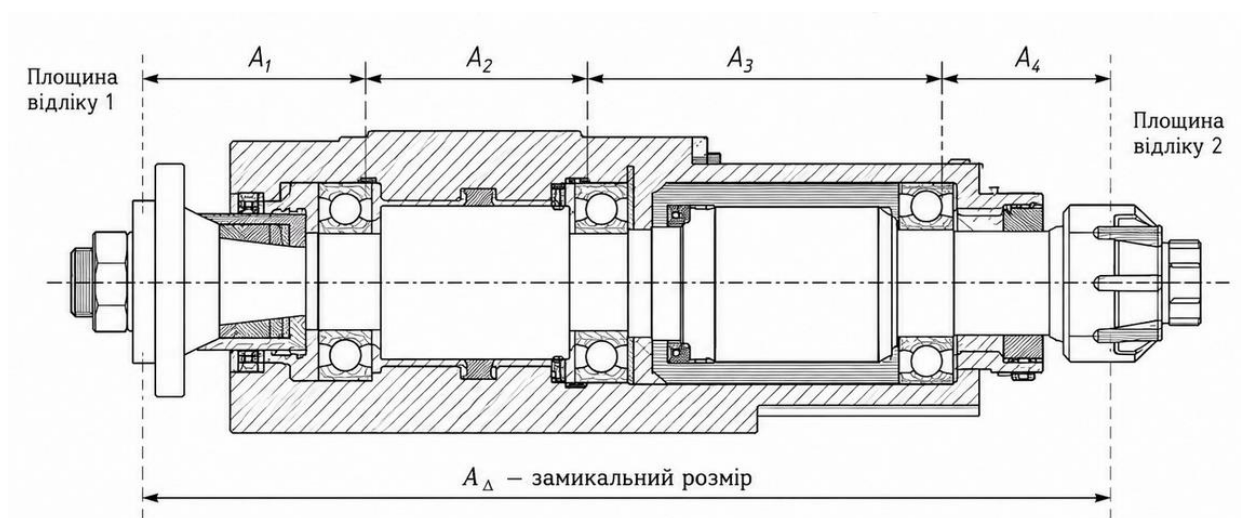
Схема розмірного ланцюга шпиндельного вузла
